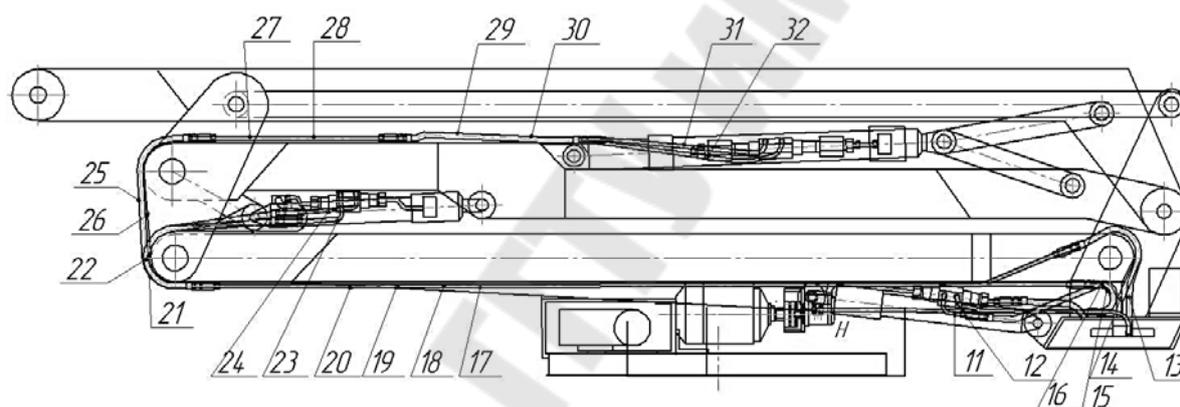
Монтажная схема трубопроводов на подъемнике
